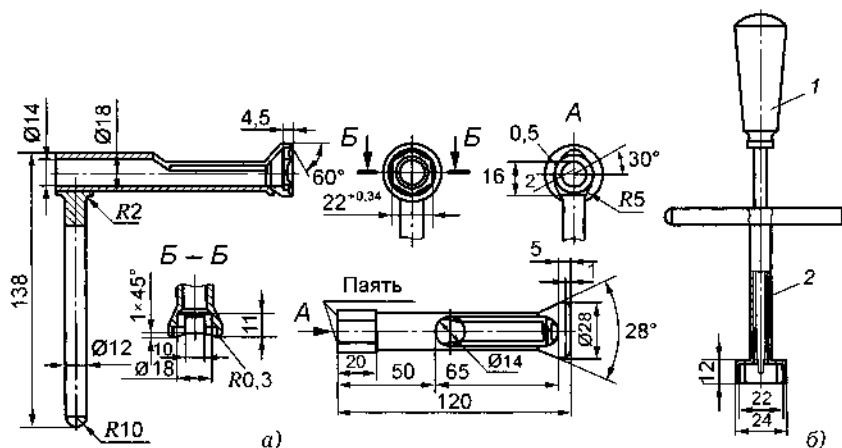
Инструмент для регулирования клапана второй ступени редуктора: а — ключ для регулировки клапана; б — отвертка с ключом; 1 — отвертка; 2 — специальный торцовый ключ
